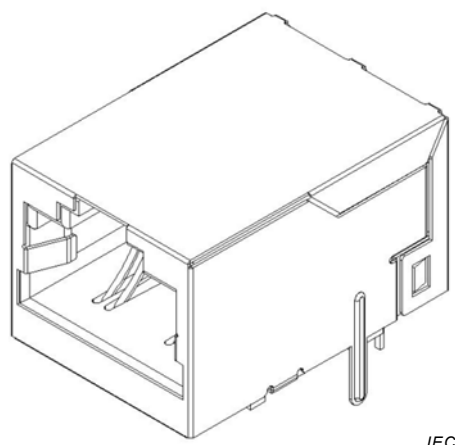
Vue isométrique d'embase à montage sur carte, exemple
